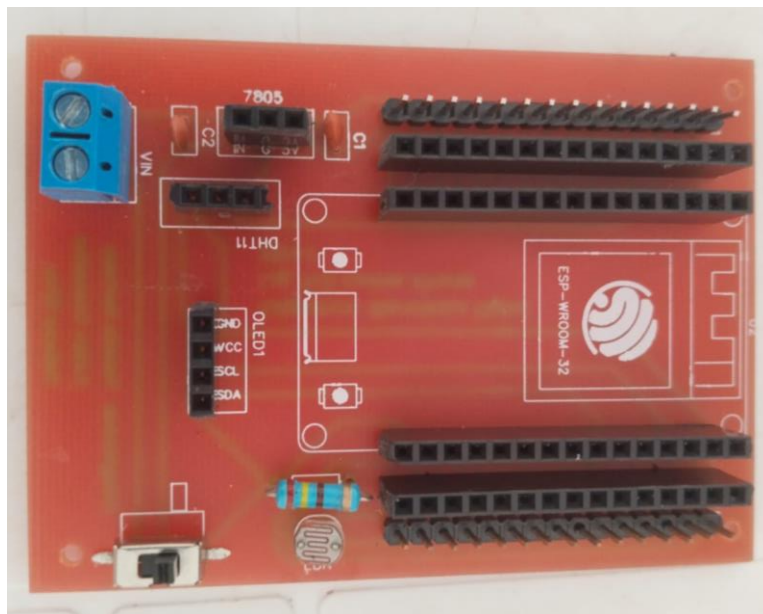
PCB ensamblada con los pines soldados.
